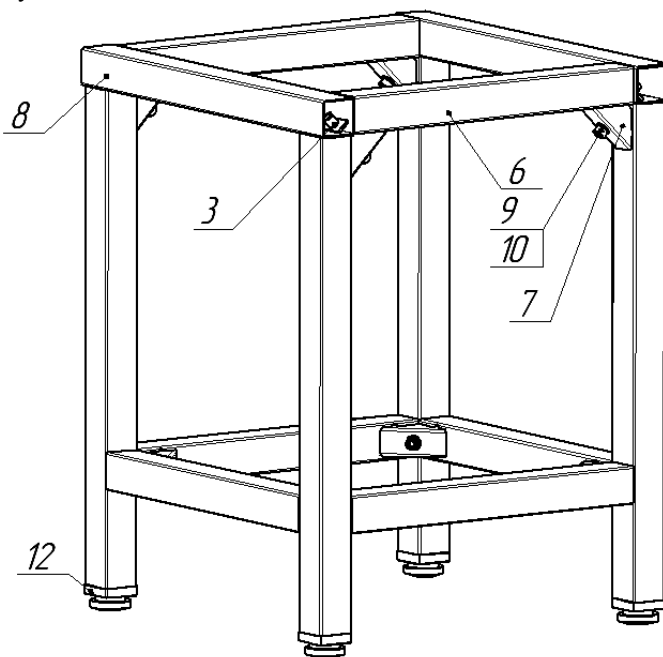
Сборка верхней части подставки и установка регулируемых опор
